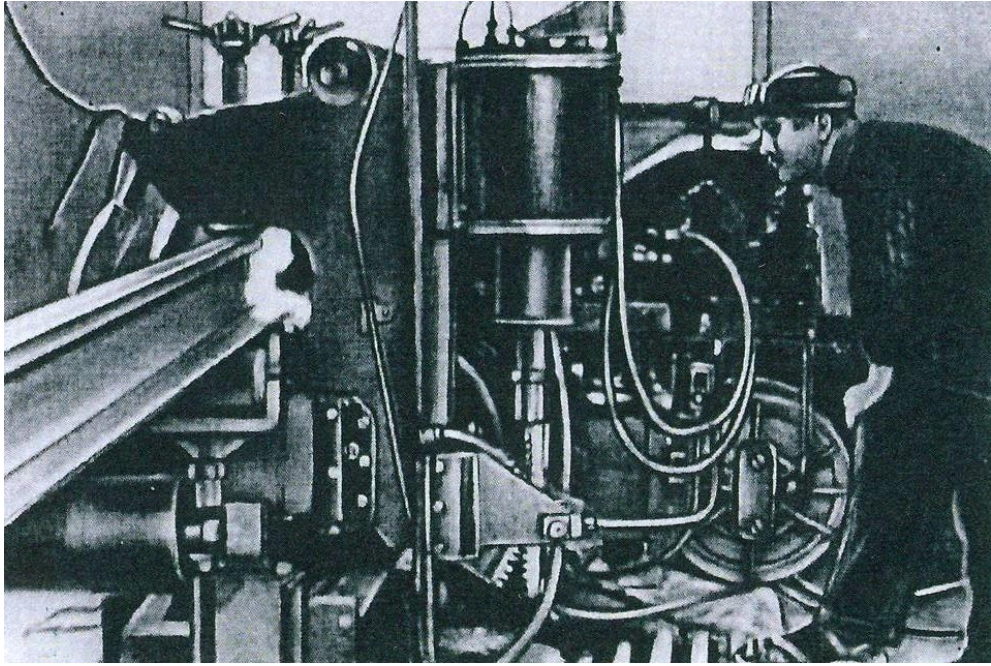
Газопрессовая сварка рельсов¹
